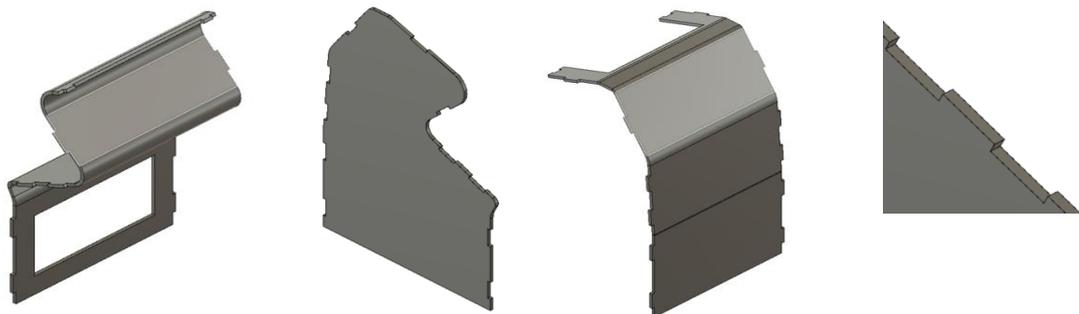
Partes tolva exterior y guías perímetro. Elaboración propia.
